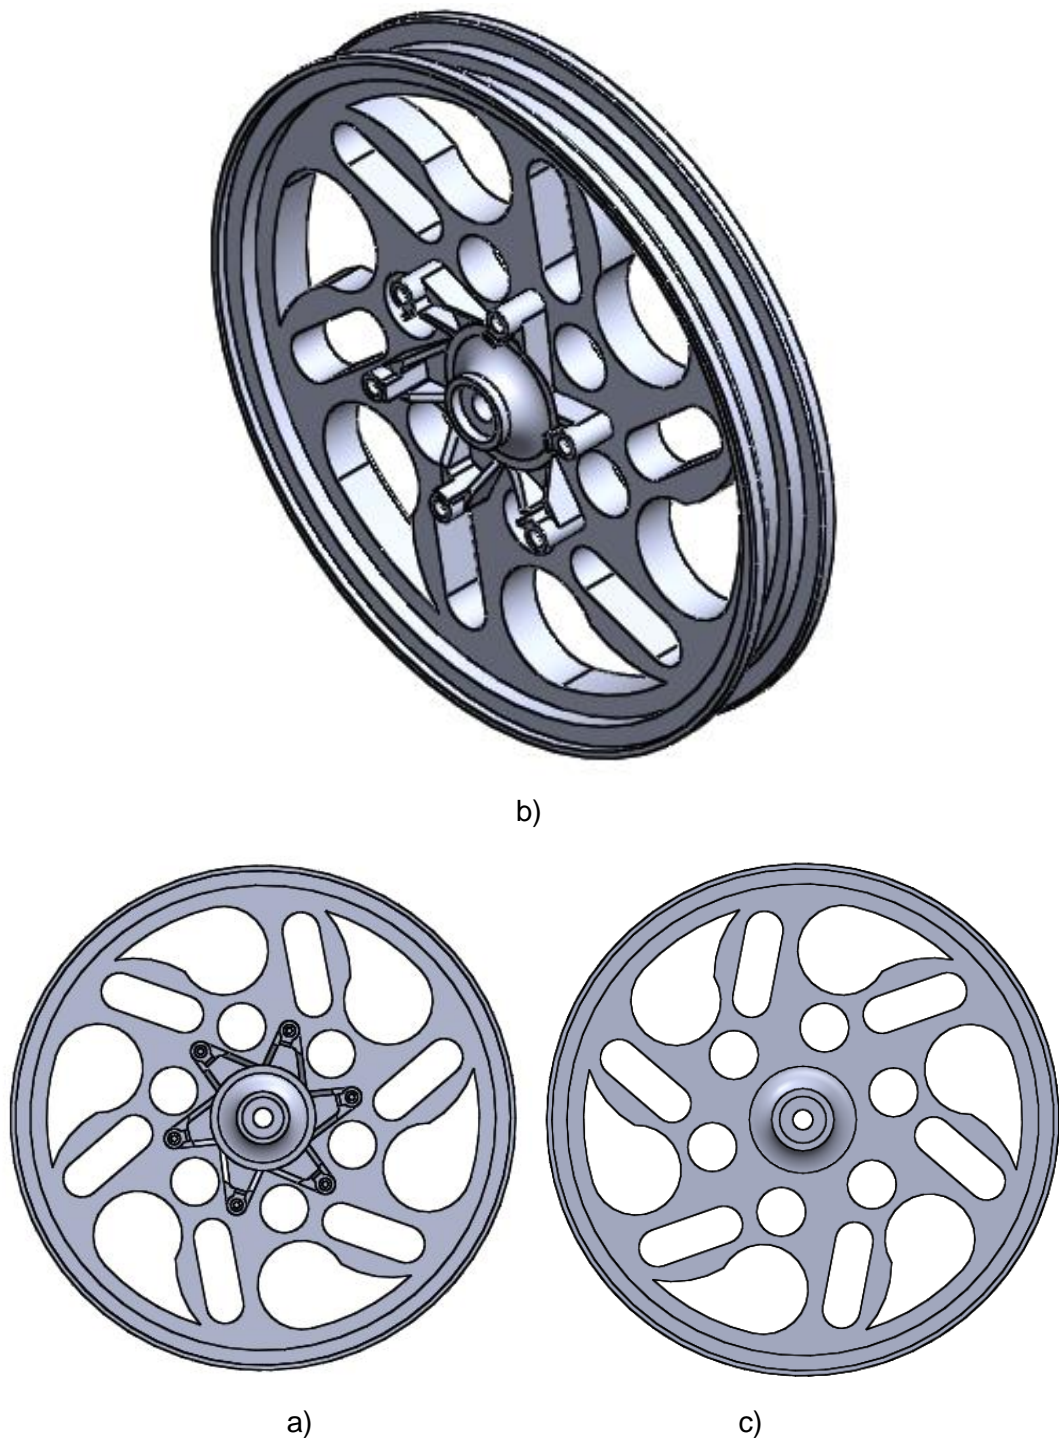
Diseño descartado “b” a) Vista frontal. b) Vista isométrica. c) Vista trasera.
